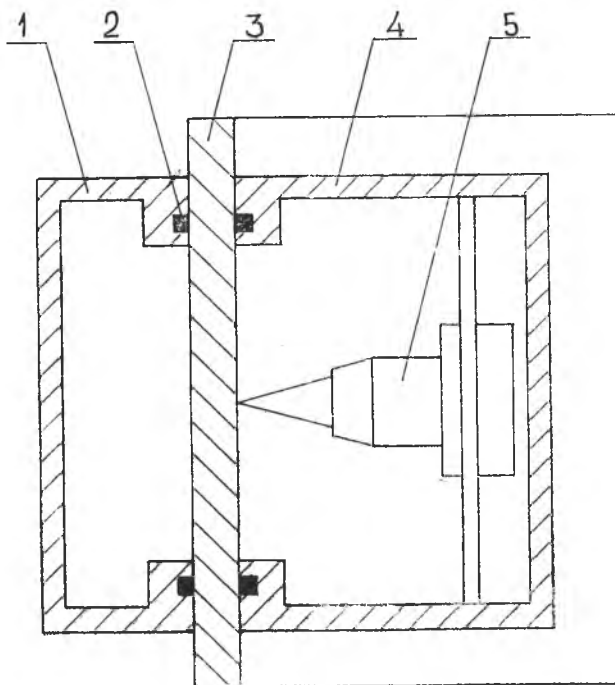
Схема электроно-лучевой сварки с местным вакуумированием: 1 — вспомогательная камера со стороны корня шва, формируемого «на весу»; 2 — вакуумные уплотнения; 3 — свариваемое изделие; 4 — основная камера со своим вакуумным уплотнением; 5 — электроно-лучевая пушка
